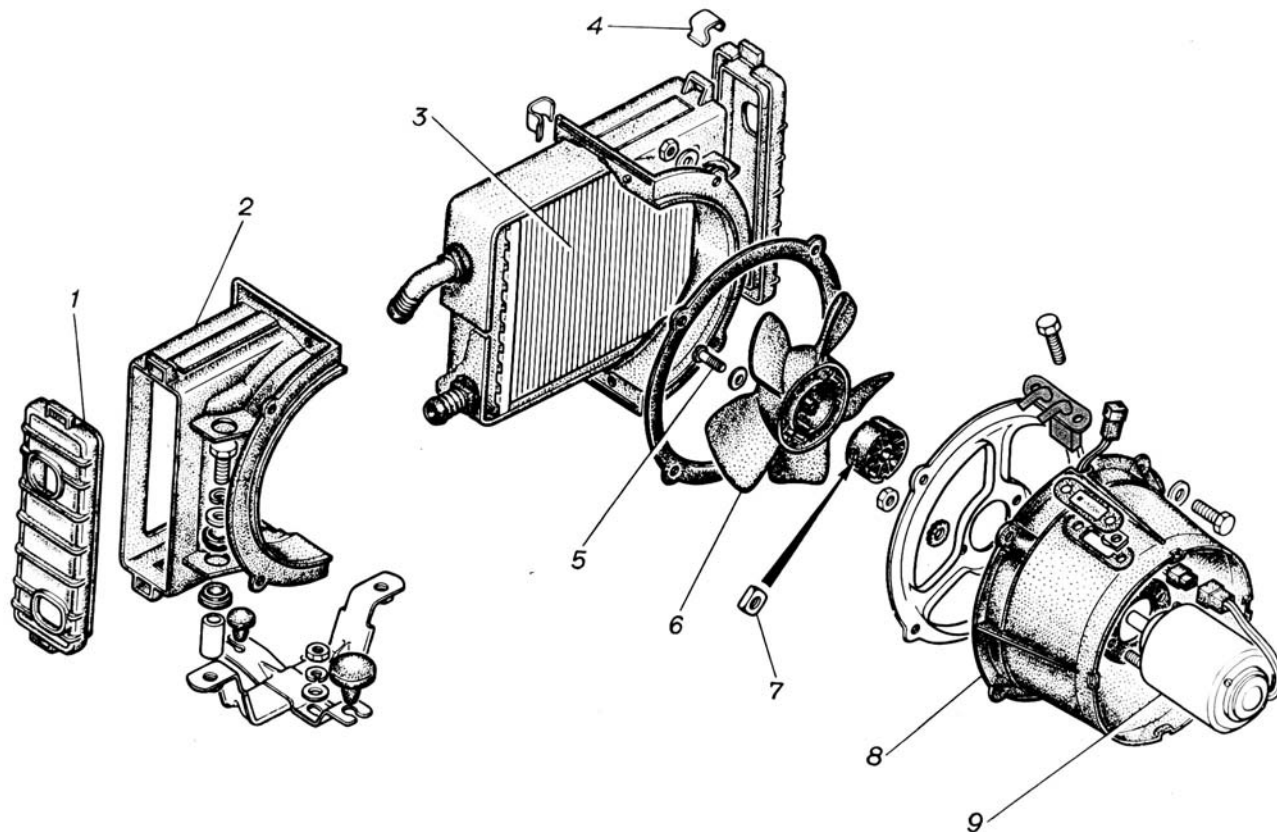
Дополнительный отопитель: 1 - крышка кожуха; 2 - кожух отопителя; 3 - радиатор отопителя; 4 - скоба; 5 - винт; 6 - вентилятор; 7 - гайка; 8 - колпак; 9 - электродвигатель
